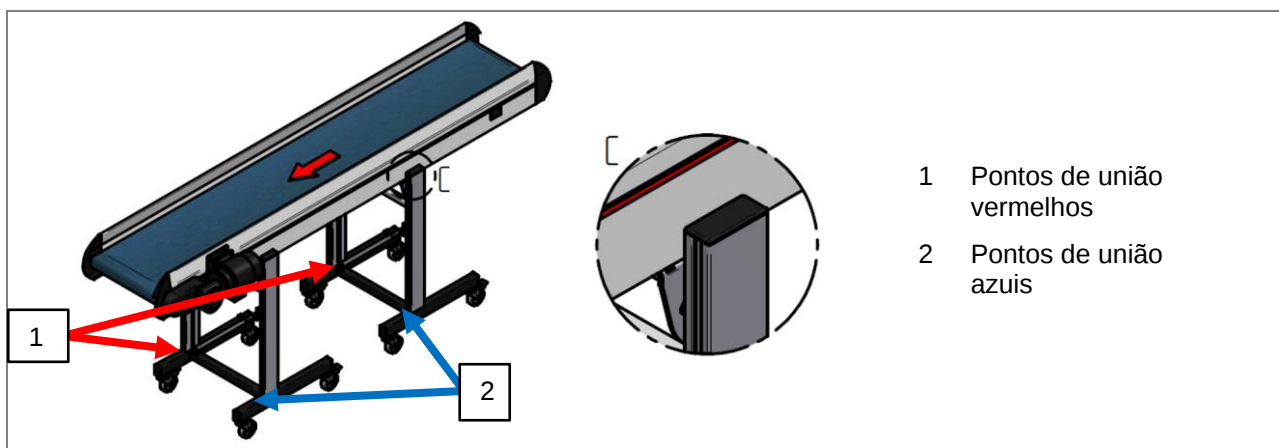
Montagem da estrutura completa do transportador de correia com estrutura inferior HE 030–HM 260 (exemplo)
